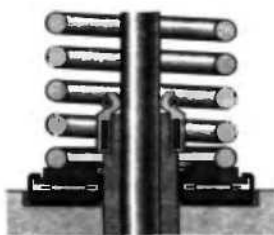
Вигляд типового рішення опори пружини клапана на підшипник, обертається
